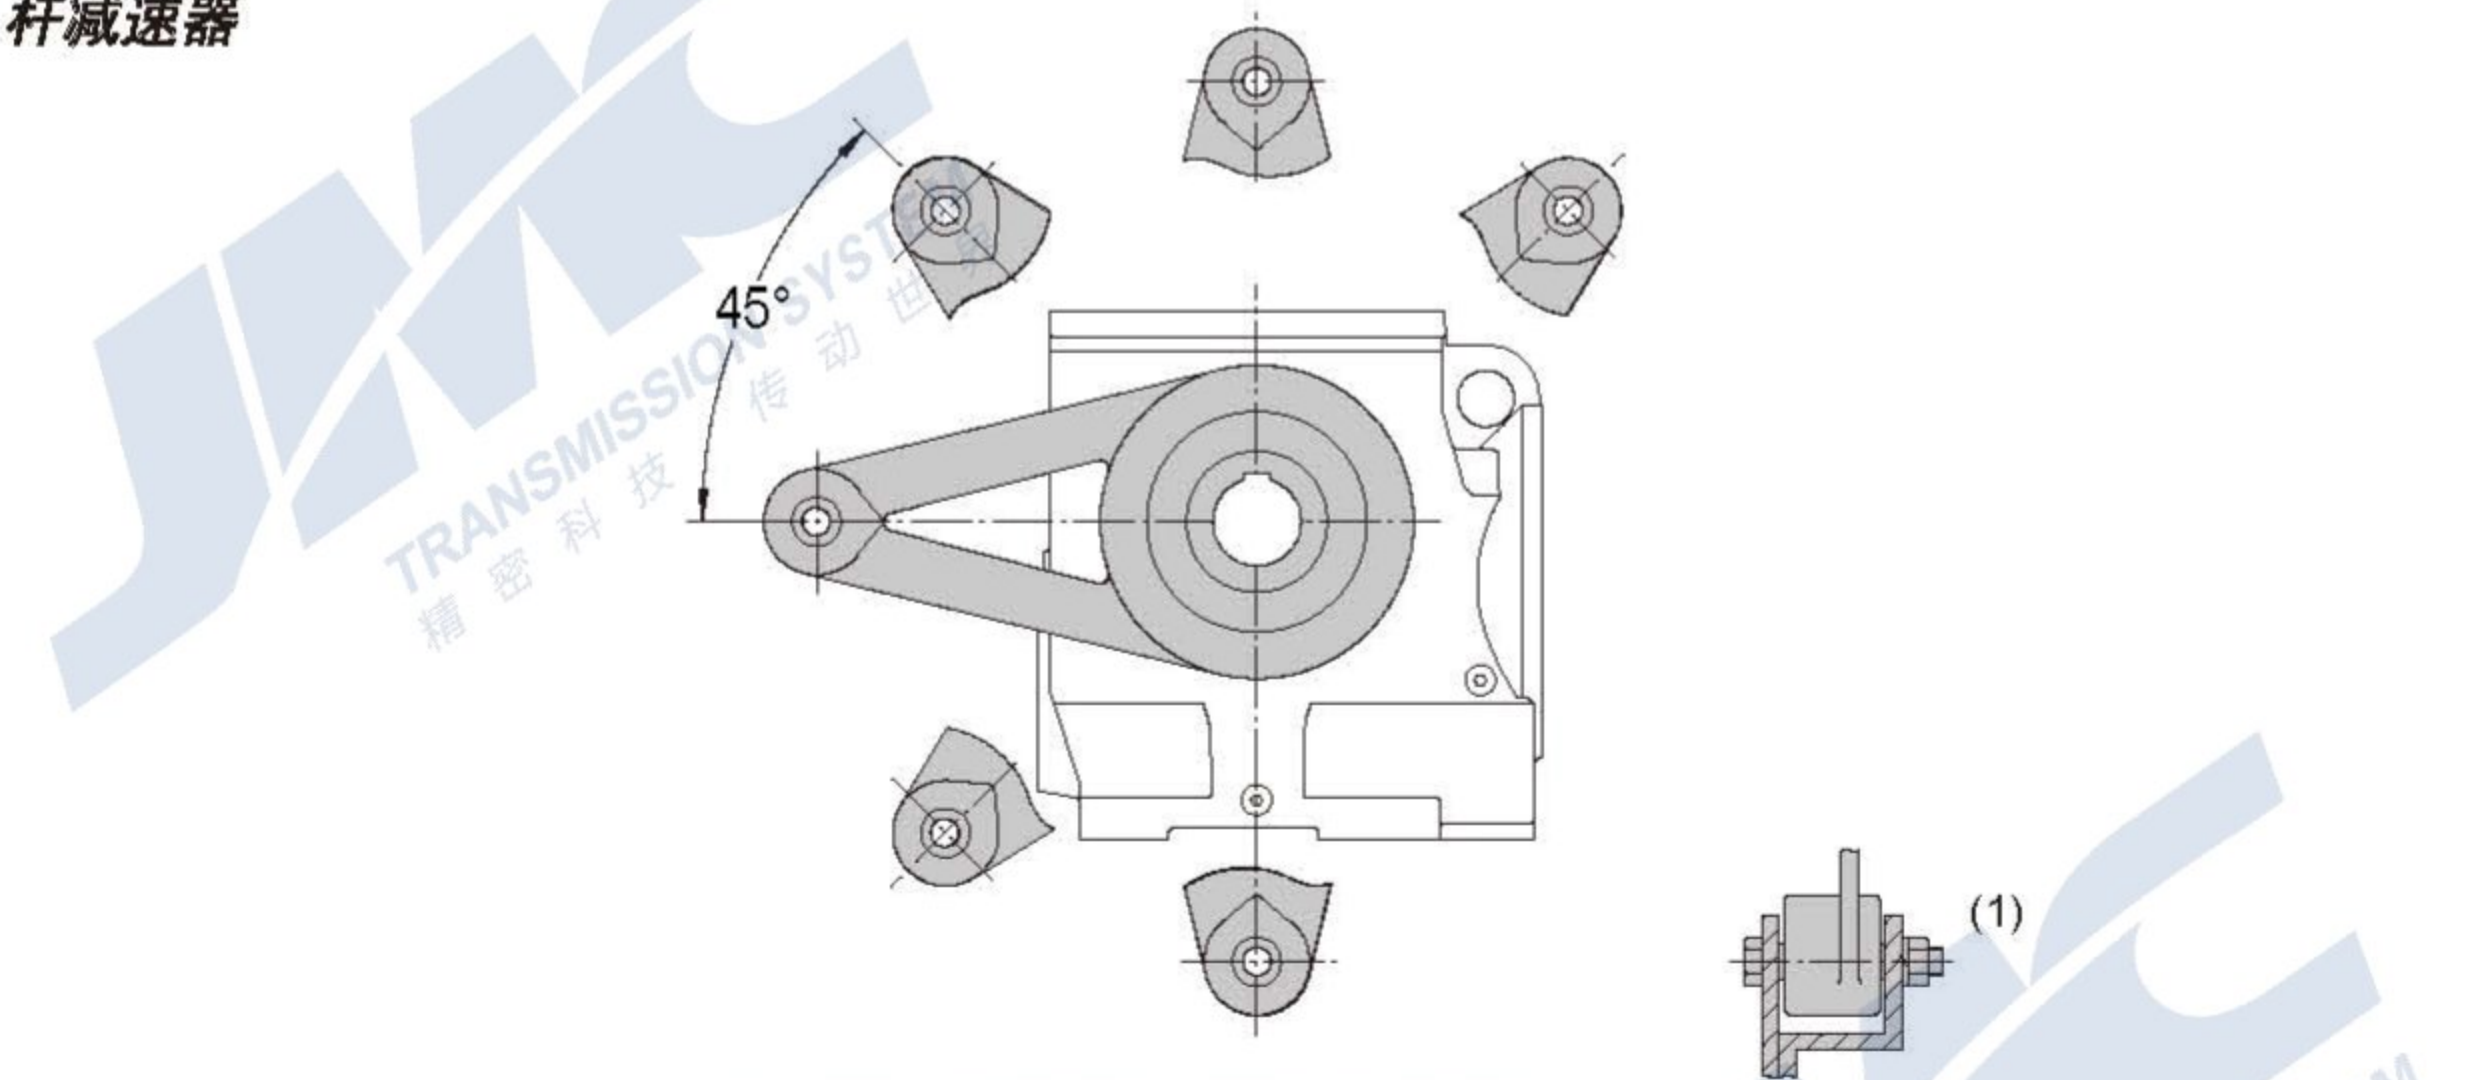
斜齿轮 - 蜗轮蜗杆减速器的扭力臂
